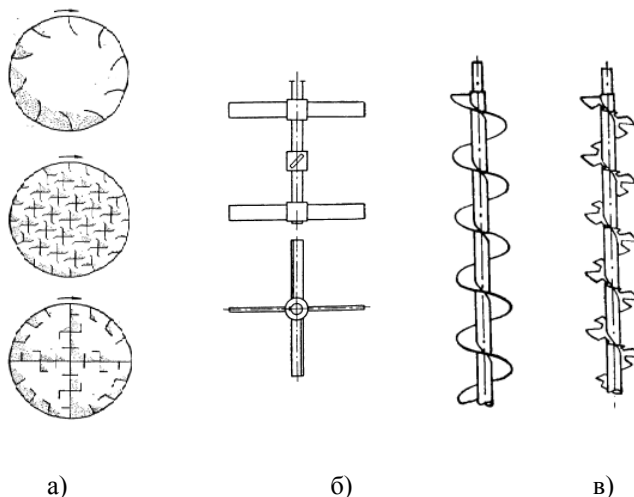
Механізми перемішування і розпушування сипких матеріалів: а) переріз сушарки барабанного типу; б) лопаті; в) шнеки
